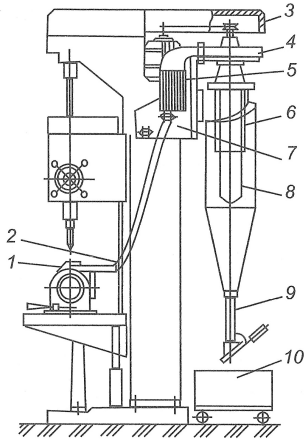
Индивидуальный пылеулавливающий агрегат:
